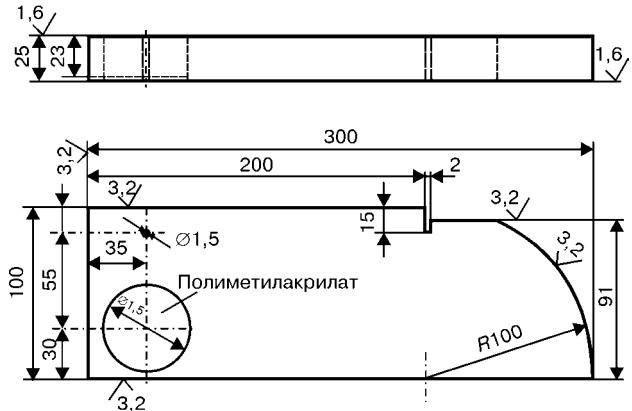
Образец для калибровки оборудования УЗ контроля (V1)
